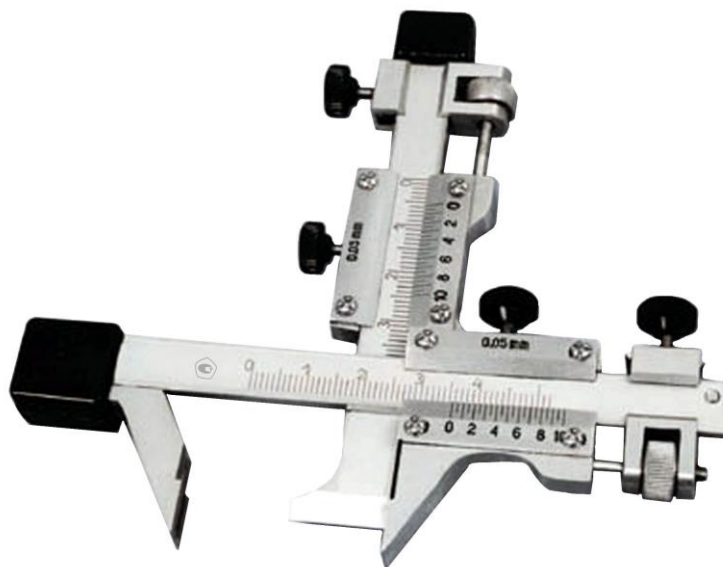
Общий вид штангензубомера с нониусами ШЗН
